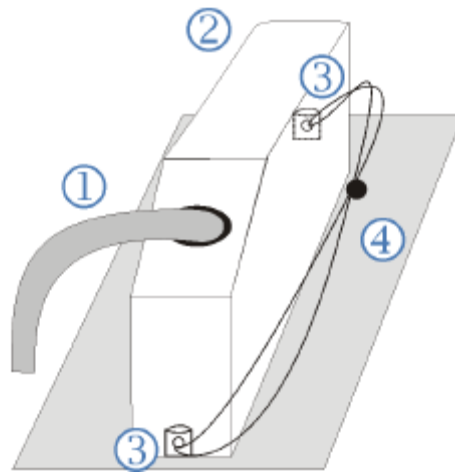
Пломбировка винтов корпуса ответного разъема плат ExMFE5 навесной пломбой
